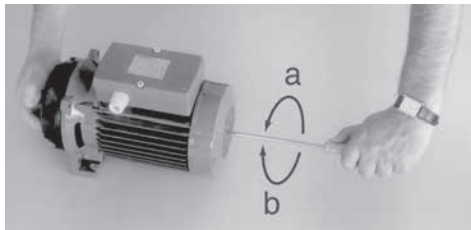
Smontaggio (a) e rimontaggio (b) girante
